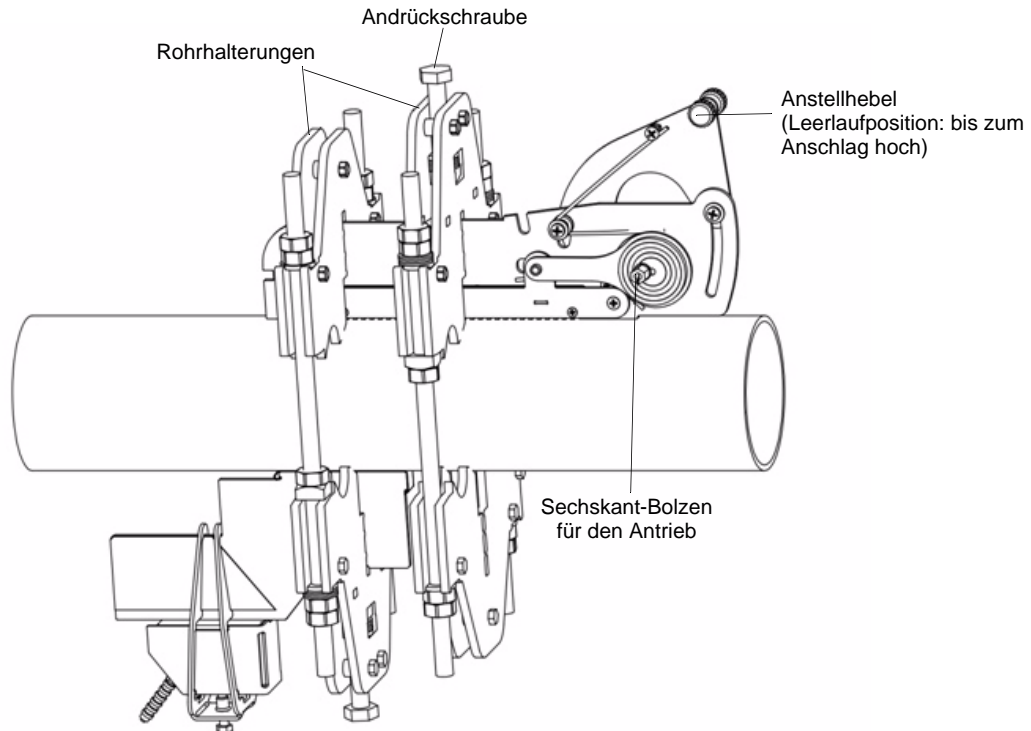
Montiertes automatisches WI-Werkzeug
